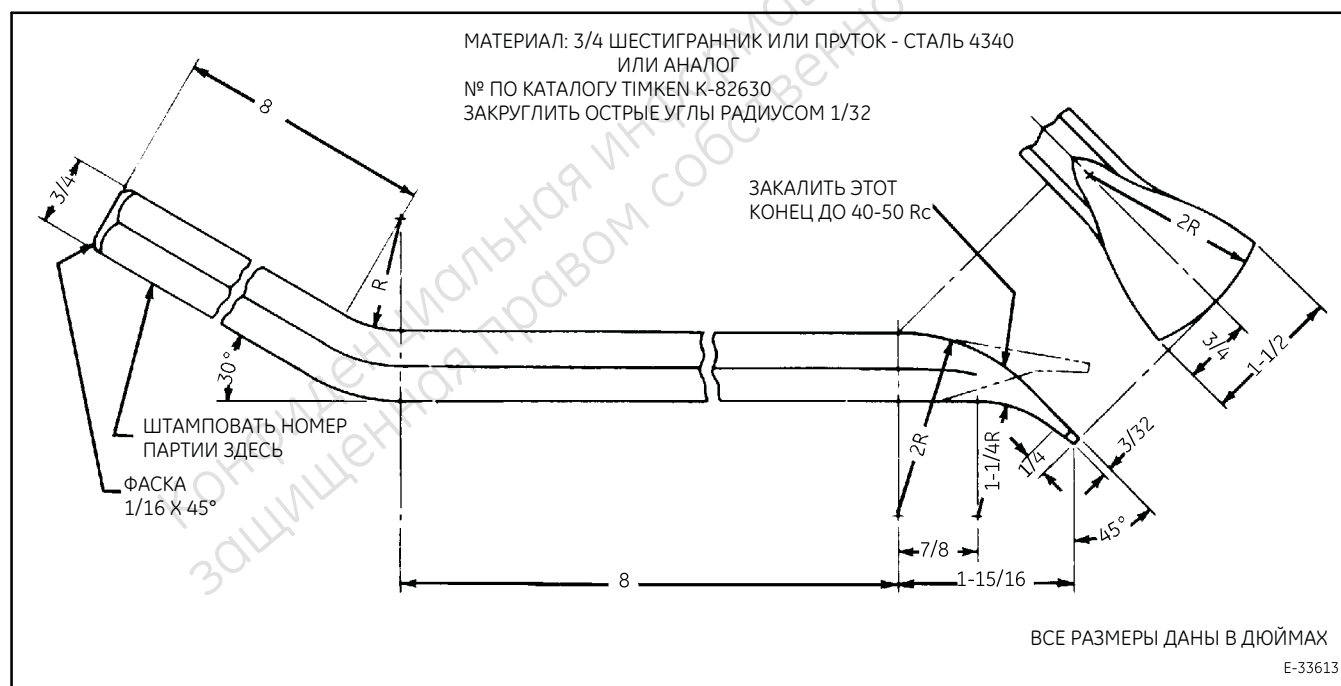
Монтажная лопатка для извлечения уплотнений из подшипников TIMKEN "AP".
